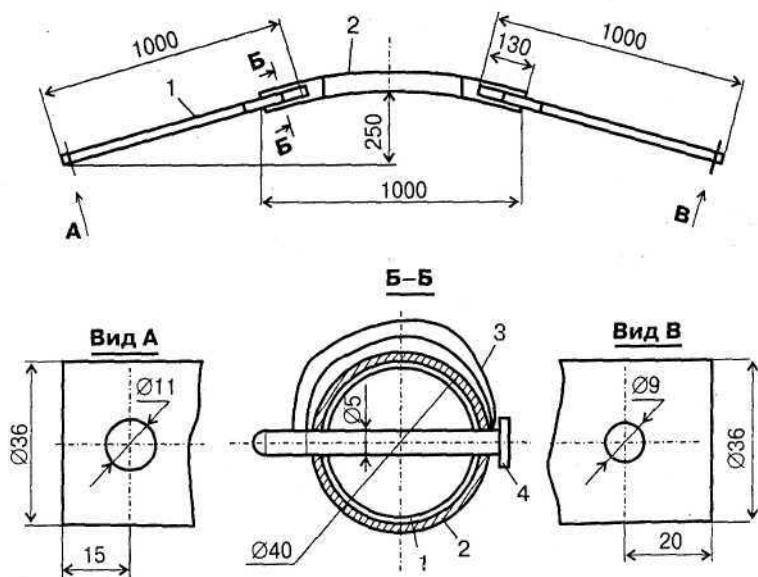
Гик: 1 — плечо, труба 36×1; 2 — колено, труба 40×1,5; 3 — связывающий шкертик; 4 — штырь Ø5
